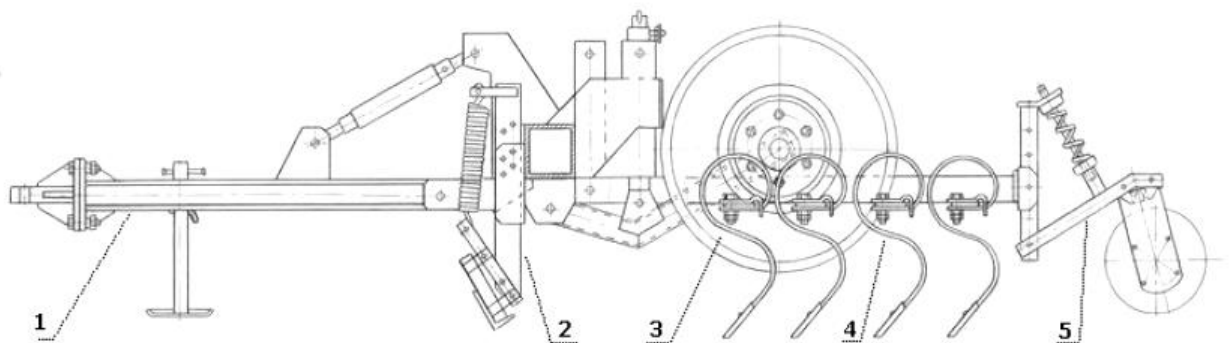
Культиватор – плоскоріз широкозахватний КПШ – 9: 1 – рама; 2 – пружинний вирівнювач; 3 – опорні колеса; 4 – робочі органи; 5 котки.
